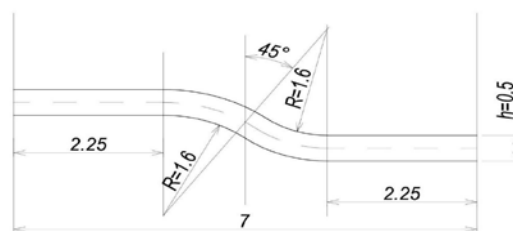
Перехідна область між розтруб та перешийок частини деталі
